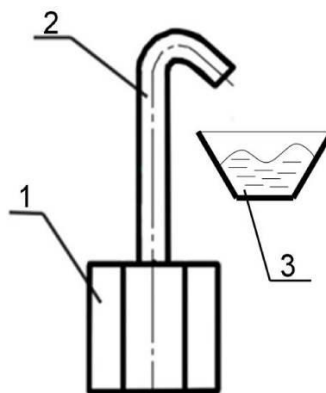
Контрольное приспособление: 1 – гайка; 2 – трубка высокого давления; 3 – емкость
